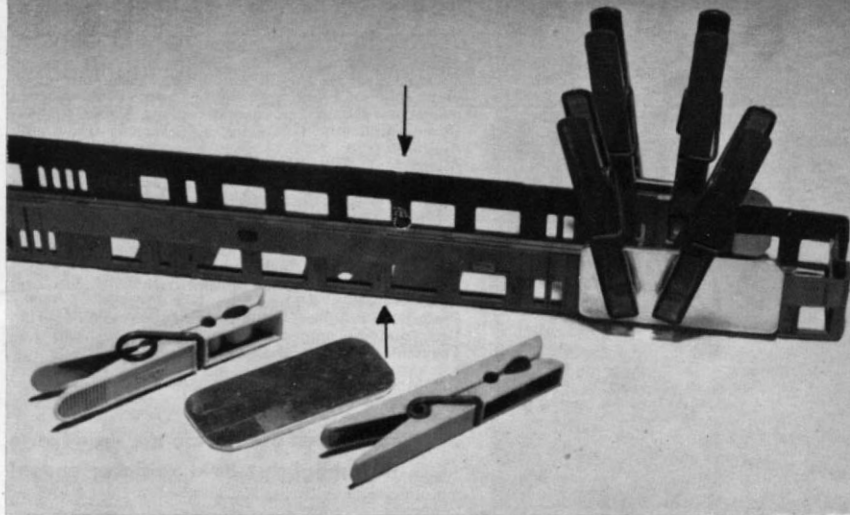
Die Wagenkastenteile werden nach dem Aufstreichen des Klebstoffes stumpf aneinandergedrückt. Damit die Außenflächen genau fluchten legt man über die Klebestellen genau plan ausgerichtete Blechstücke (z. B. 2 mm Alu-Blech) und preßt diese mit Wäscheklammern fest an die Wagenkastenwände an. Dann mindestens 24 Stunden trocknen lassen, auch wenn Plastikkleber verwendet wurde!
